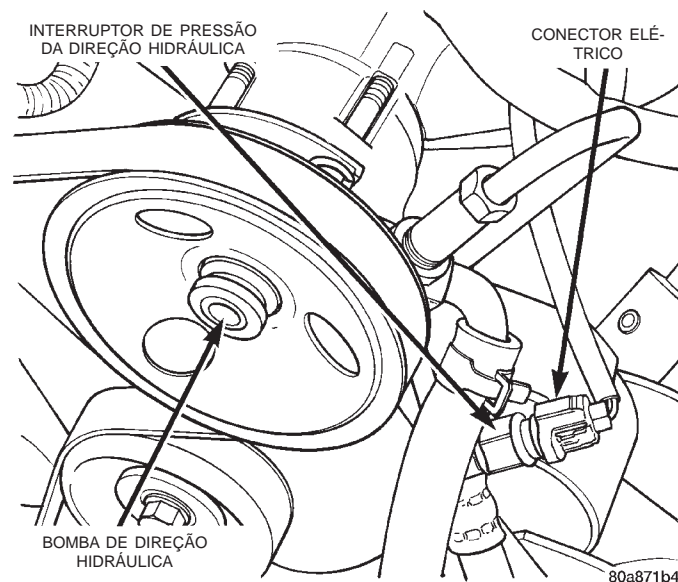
Interruptor de Pressão da Bomba de Direção Hidráulica—Motor 2.5L
